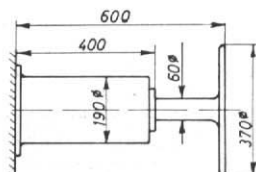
Hülsenpuffer mit Kegel- oder Ringfeder für 32 bzw. 35 t Endkraft und 75 mm Hub, sowie 370 bzw. 450 mm Pufferteller- ϕ für 2- bzw. 4-achsige Güterwagen.
